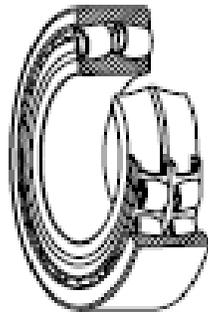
Rodamientos de rodillos esféricos
